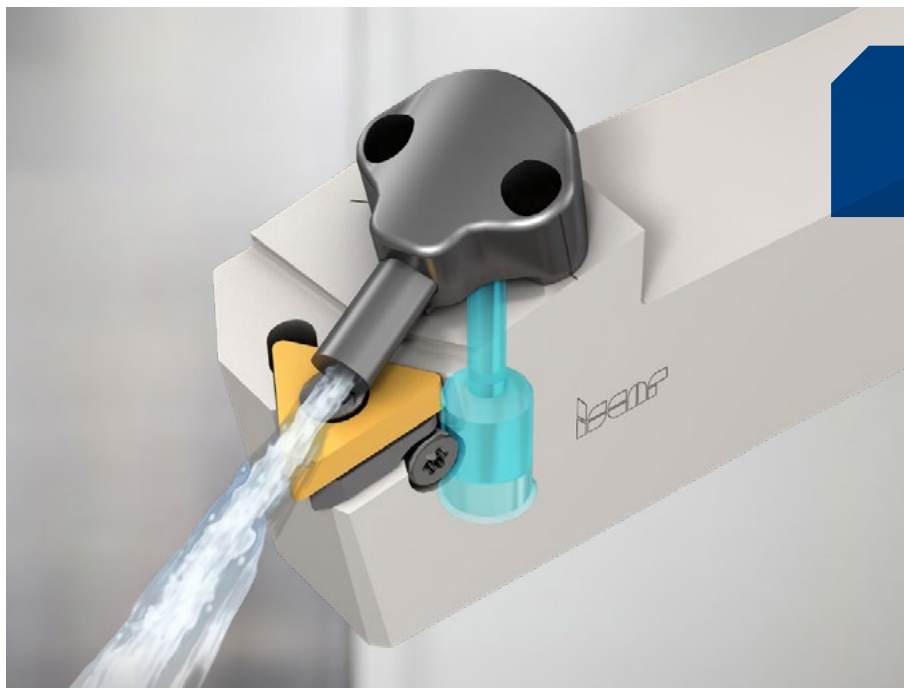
Різець ISCAR із внутрішньою подачею ЗОР для ефективного контролю стружки
